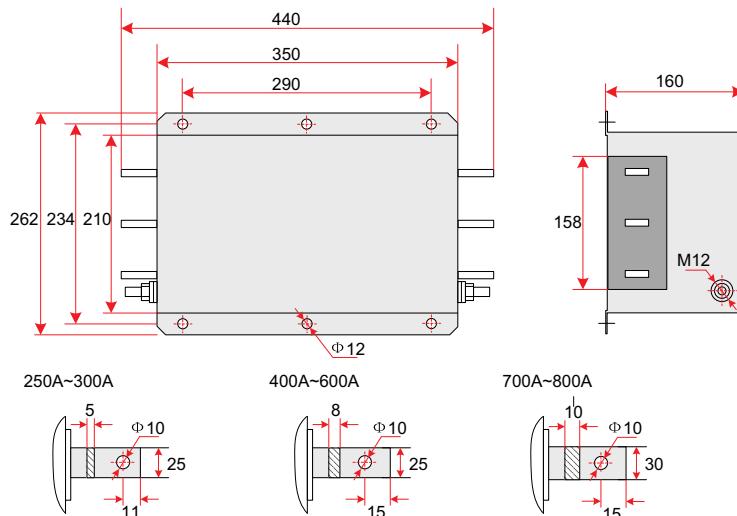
坚力滤波器250~800A尺寸图(单位: mm)
